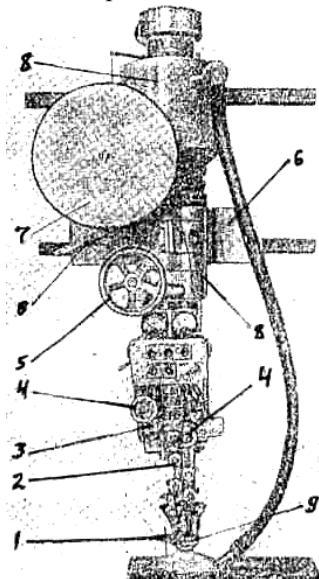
Универсальный сварочный аппарат АБС:
